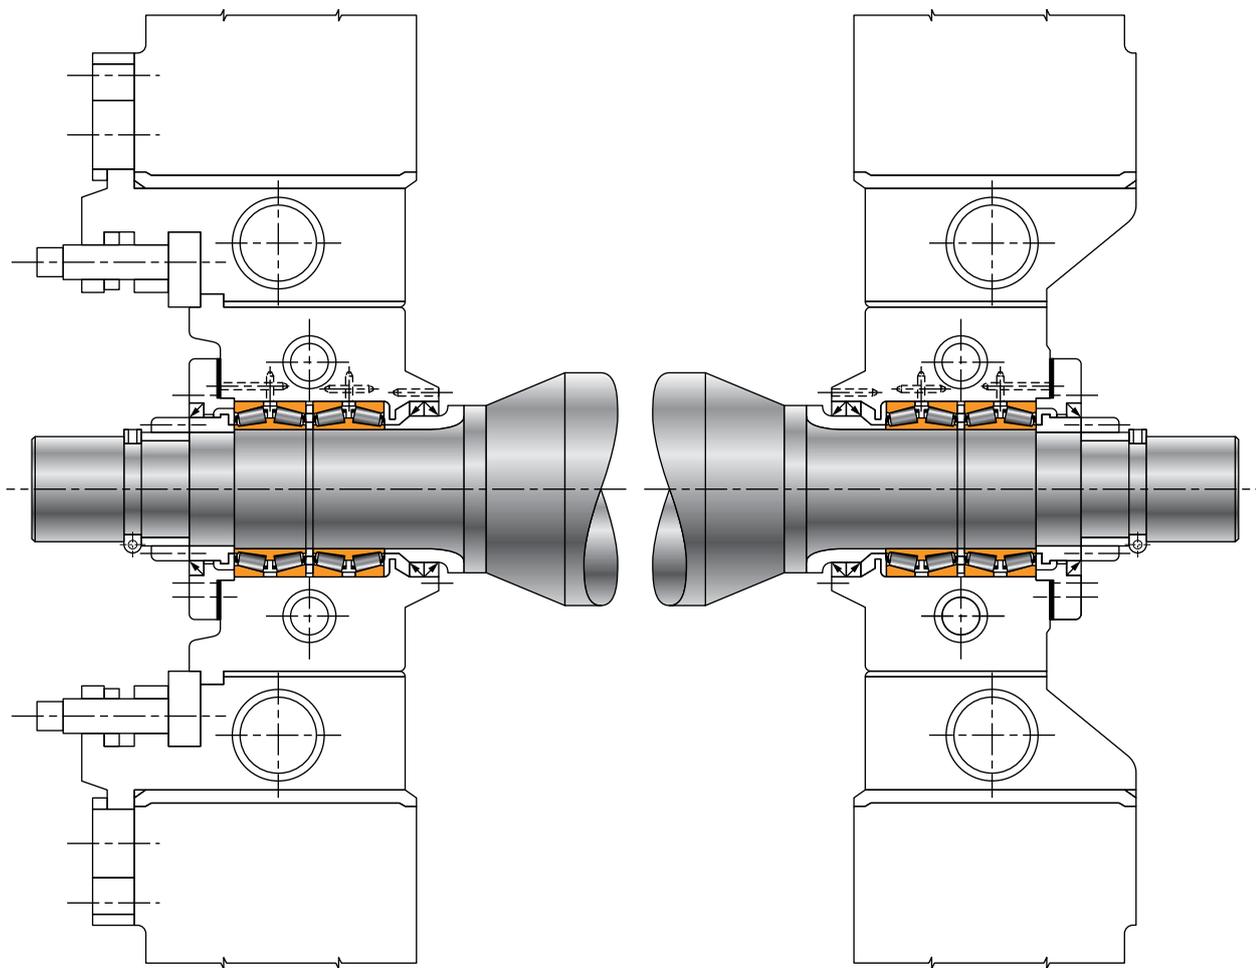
工作辊轴承座在支撑辊轴承座支脚上的安装结构
